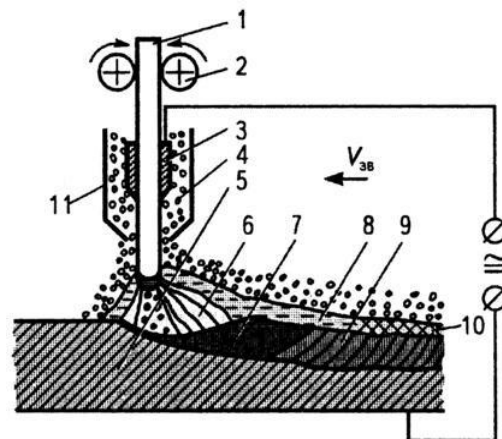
Схема автоматичного зварювання під флюсом:
